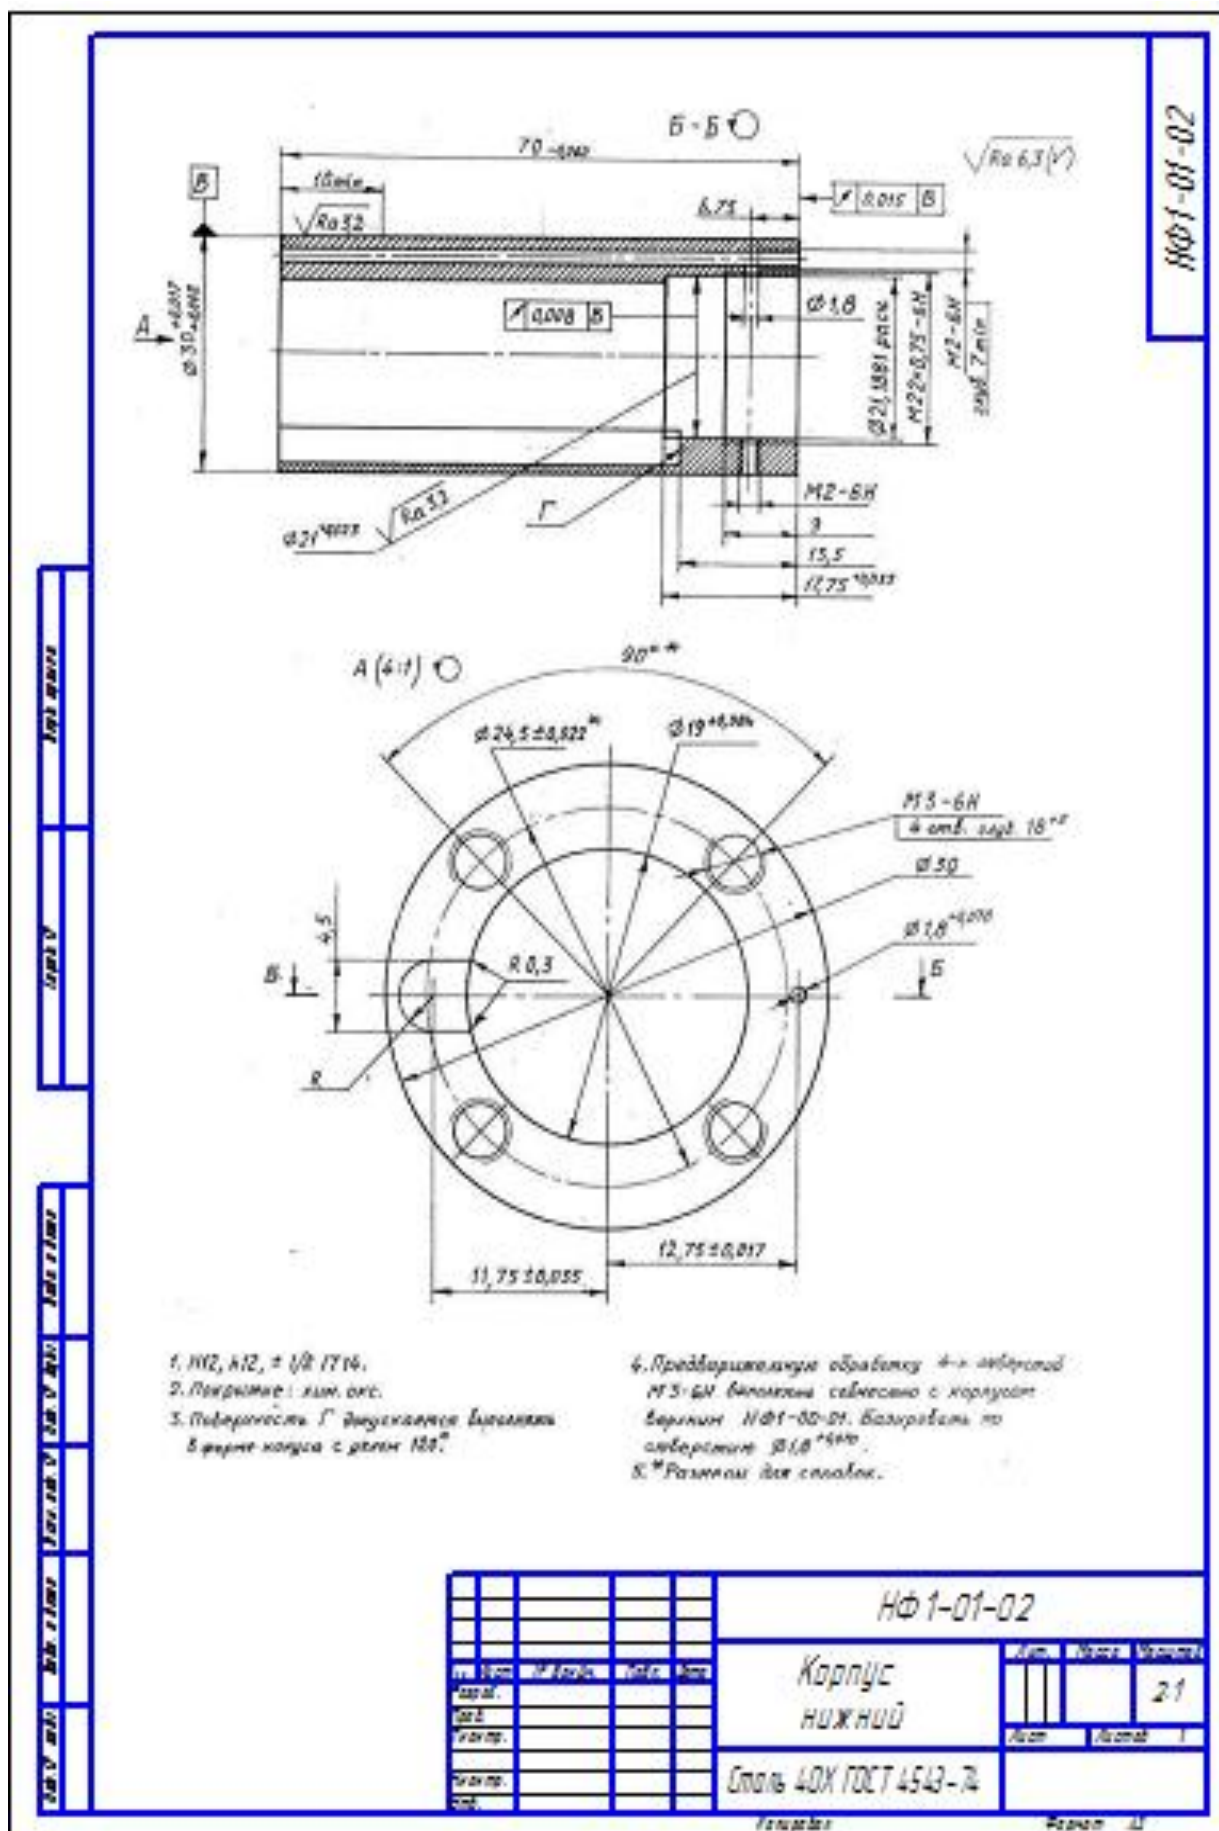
Пример выполнения рабочего чертежа детали «Корпус нижний»
